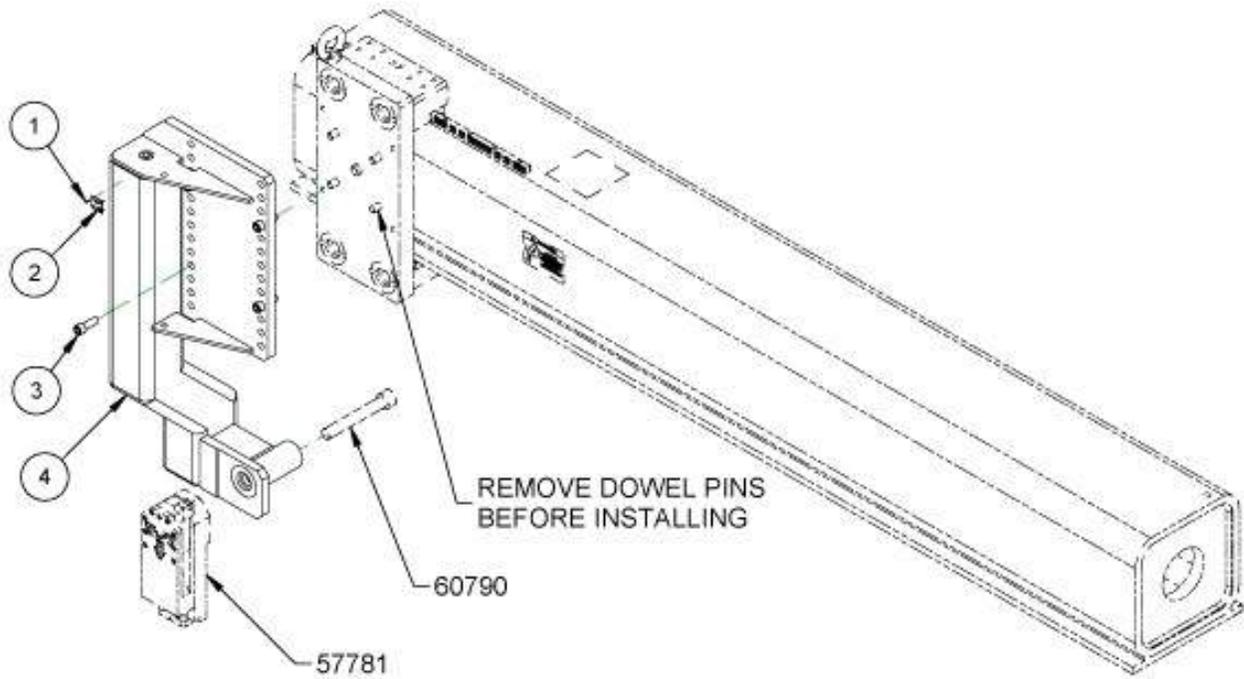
ENSEMBLE DE FREIN À TRAINÉE (P/N 62535)
